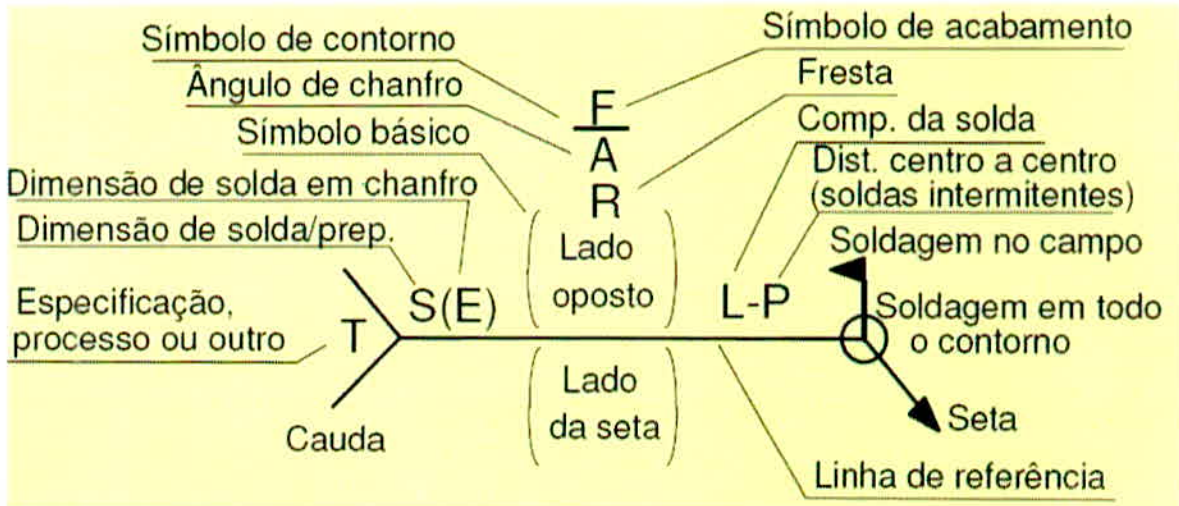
Localização dos elementos de um símbolo de soldagem.
